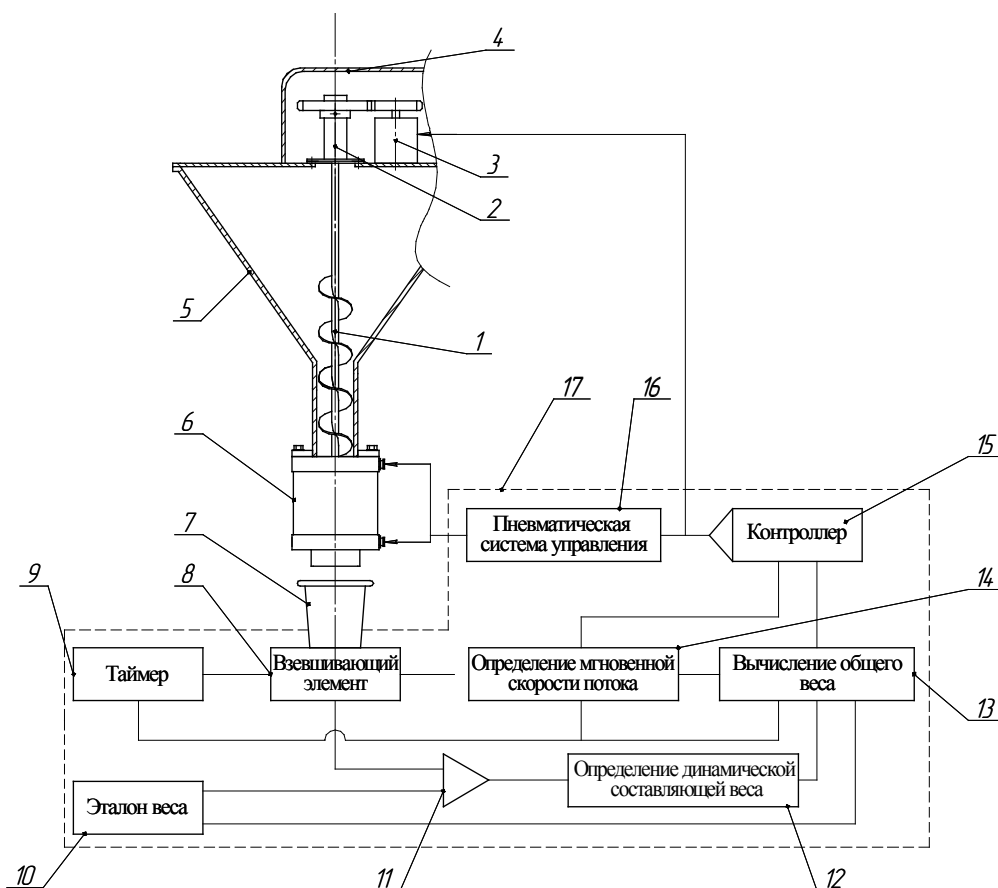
Схема мехатронного модуля весового дозирования вязкопластической продукции: 1 - шнек; 2 - приводной механизм; 3 - привод; 4 - крышка; 5 - бункер; 6 - телескопический патрубок; 7 - тара; 8 – взвешивающий элемент; 9 - таймер; 10 - эталон веса; 11 - компаратор; 12 - блок определения динамической составляющей веса; 13 - блок вычисления общего веса; 14 - блок определения мгновенной скорости потока; 15 - контроллер; 16 - пневматическая система управления; 17 - система управления
